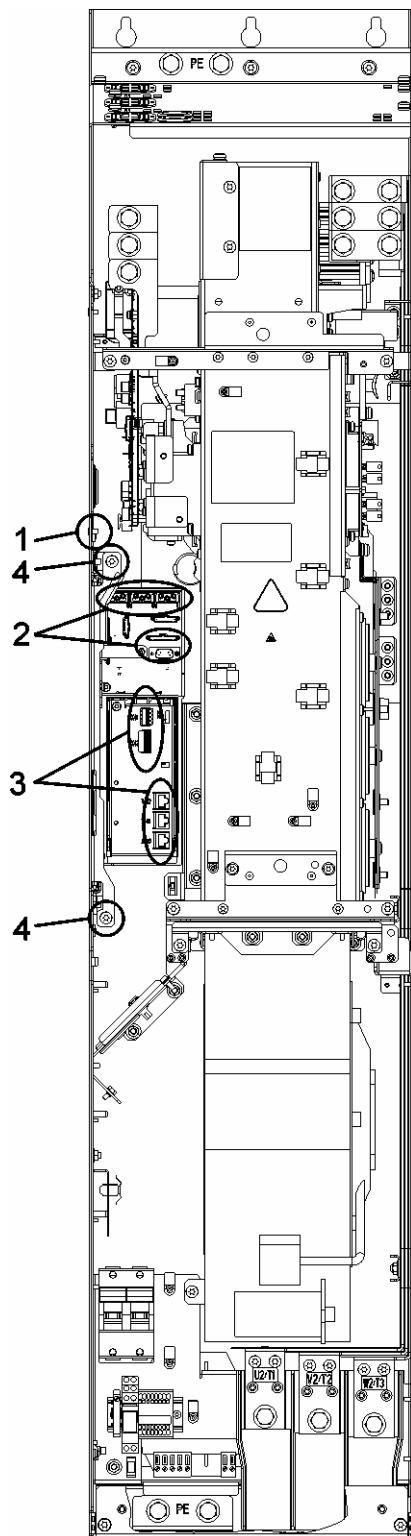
Замена платы Control Interface Board, типоразмер GX
